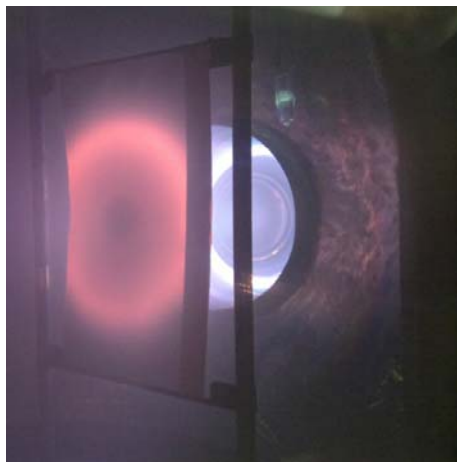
Фотография пучка и обрабатываемой детали (лист стали толщиной 1 мм)
